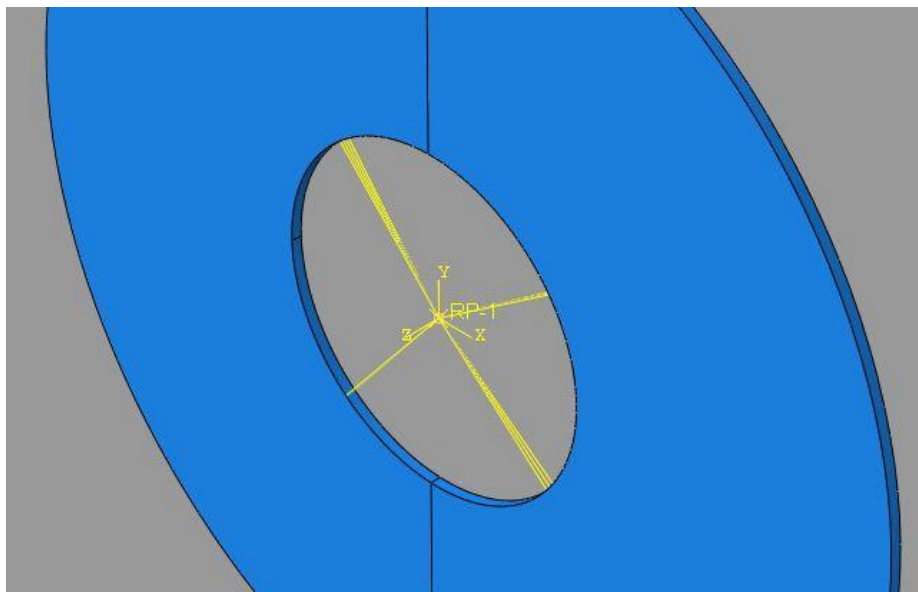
Detalhe do acoplamento utilizado na fixação da engrenagem
